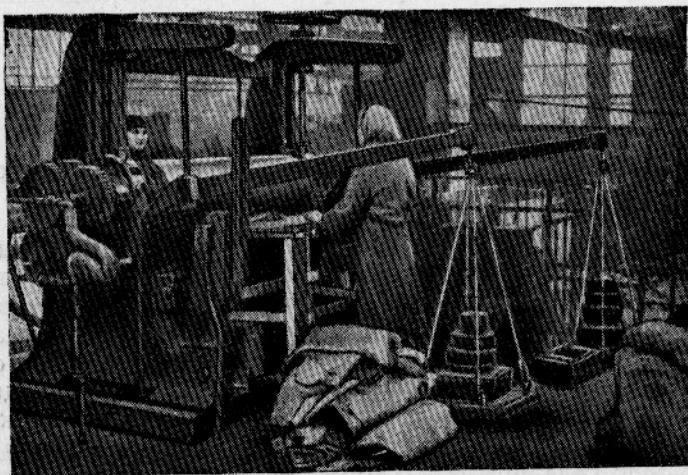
Однопарный вальцовый пресс—реконструированный гладильный каландр, установленный на кожевенном заводе им. Л. М. Кагановича.
